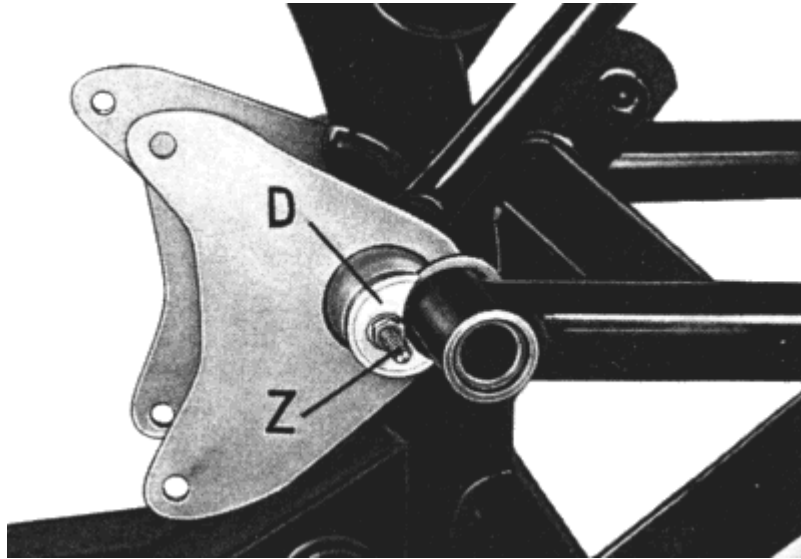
Motorbefestigungsbleche durch Druckring (D) und Zugspindel (Z) mit Gewinde M 6 axial zusammengedrückt, Hinterradschwinge aufgeschoben
